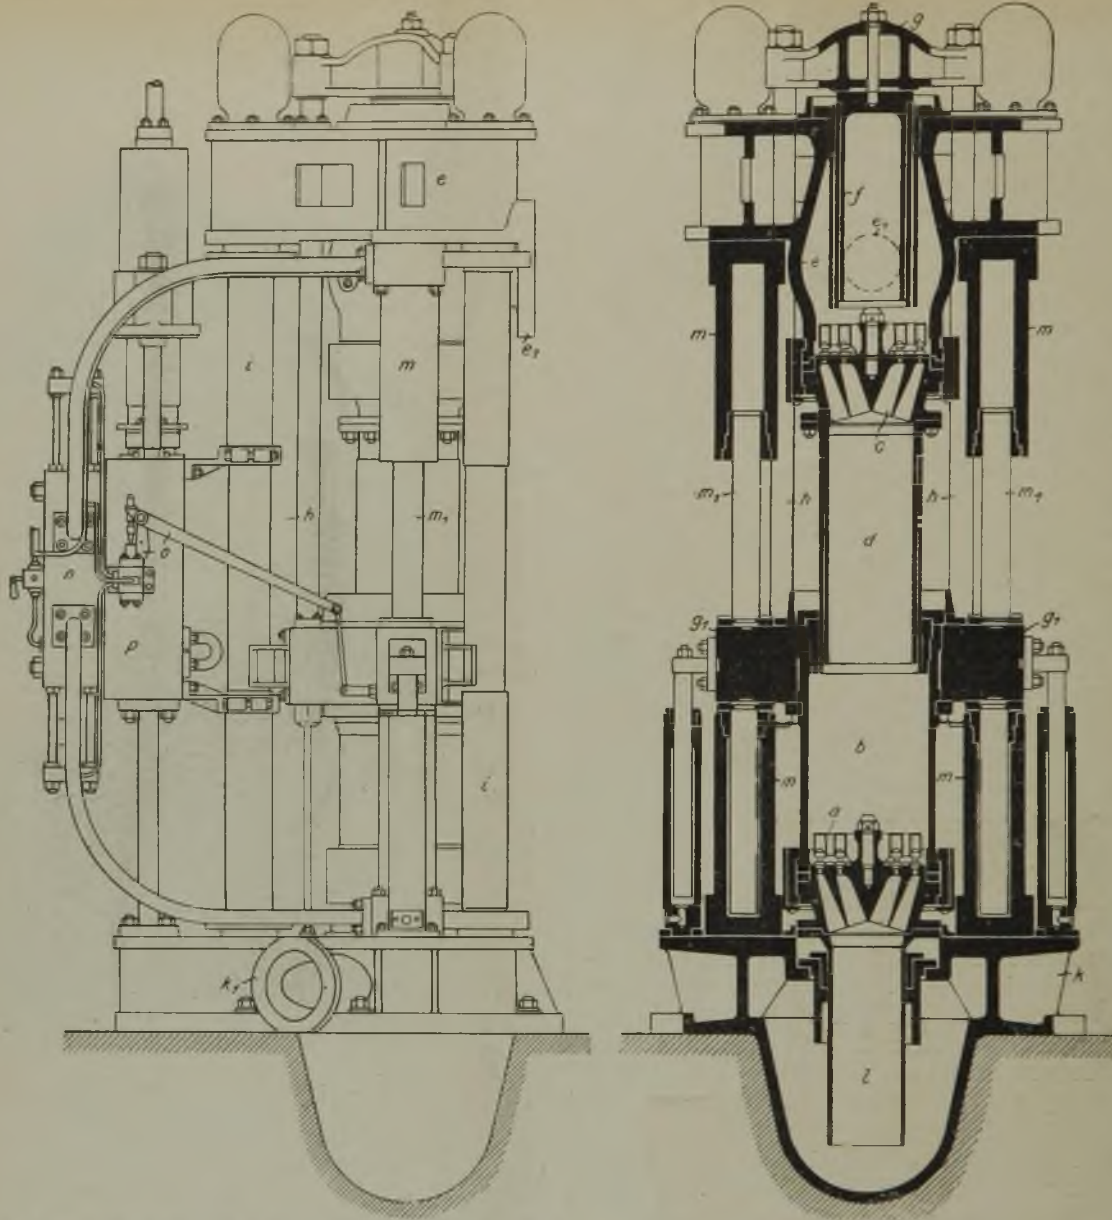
Ansicht und Längsschnitt der hydraulisch betriebenen Pumpe auf Zeche Christian Levin.
